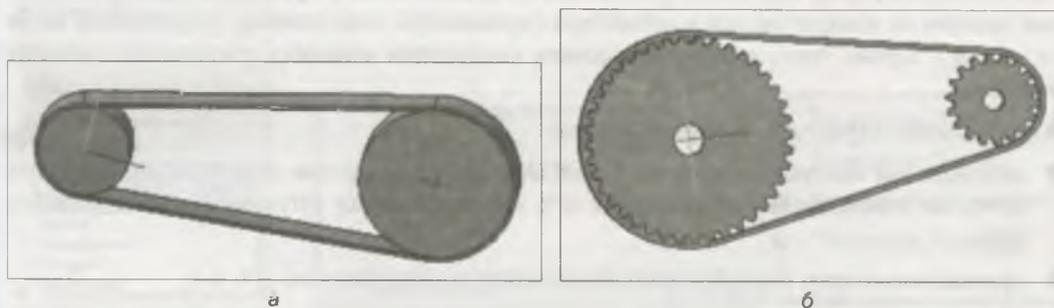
Сборки: Ременная передача (а); Зубчатая передача (б)
